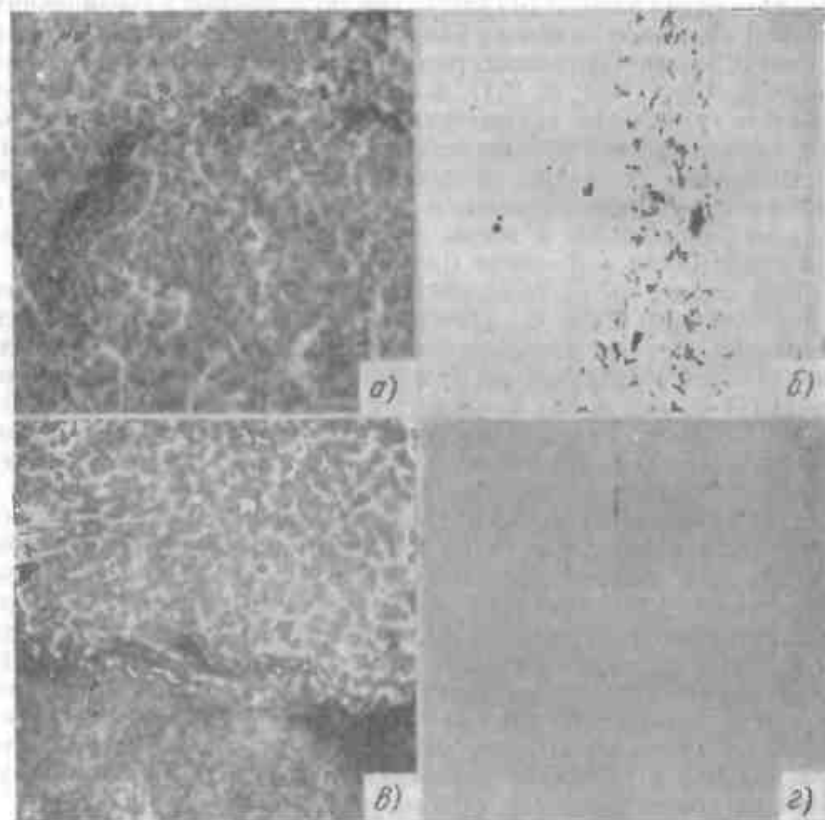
Дефекты в стыке при сварке оплавлением стали с недостаточной осадкой:
